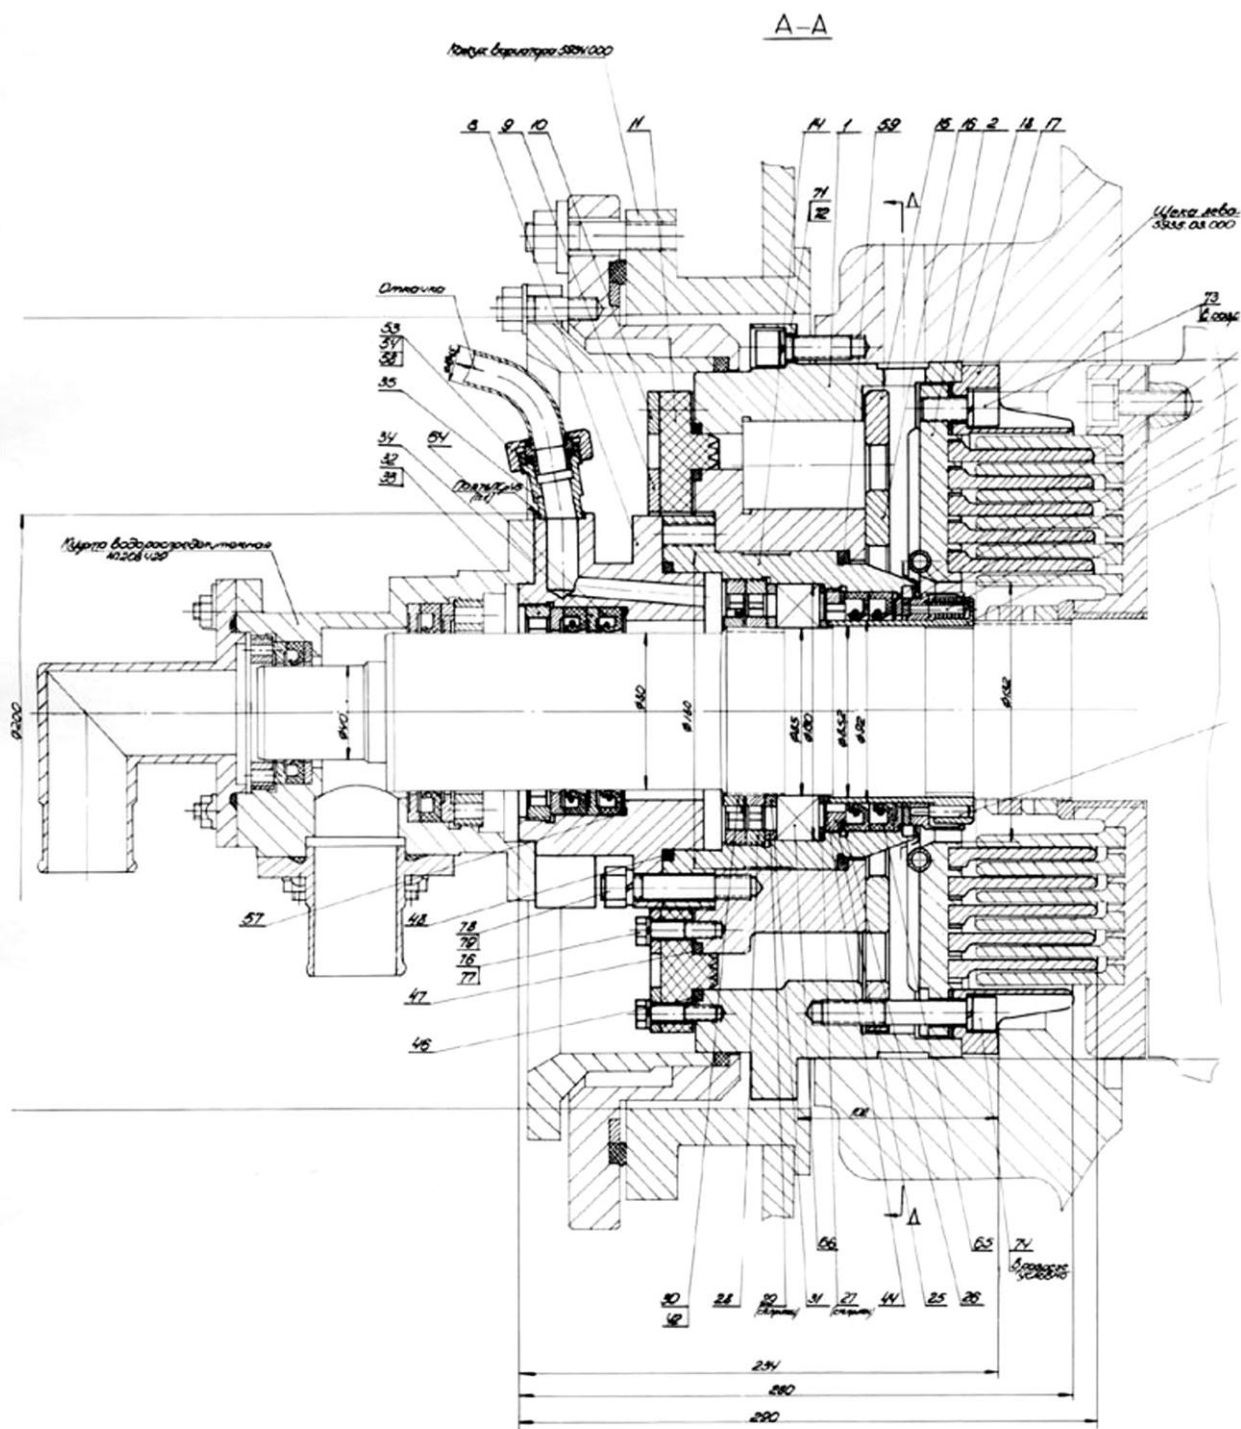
Подшипниковый узел наружного конца левого вариатора
